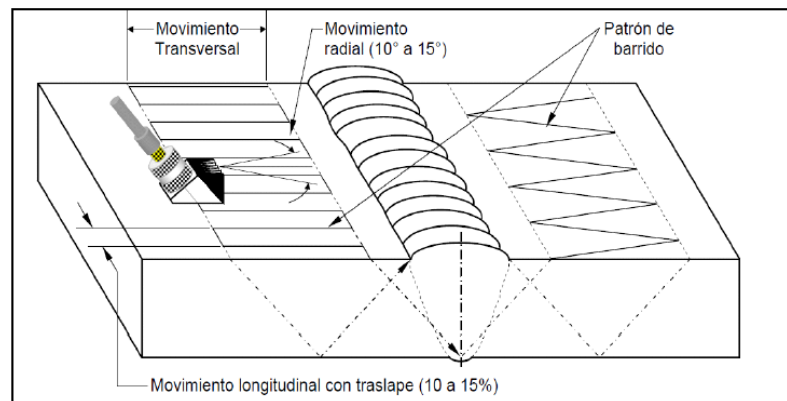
Patrones de barrido en una junta soldada. Fuente [20]
